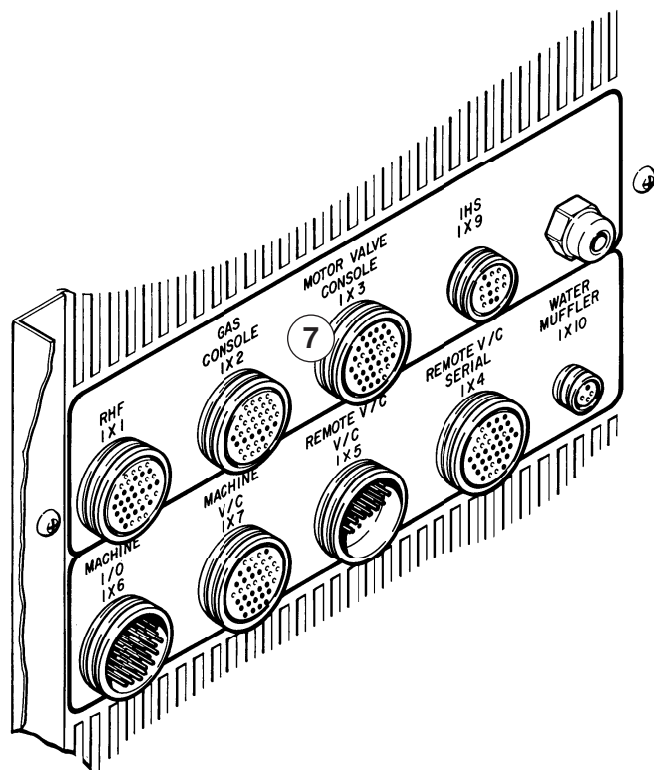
Collegamenti dall'alimentatore alla console del gas
